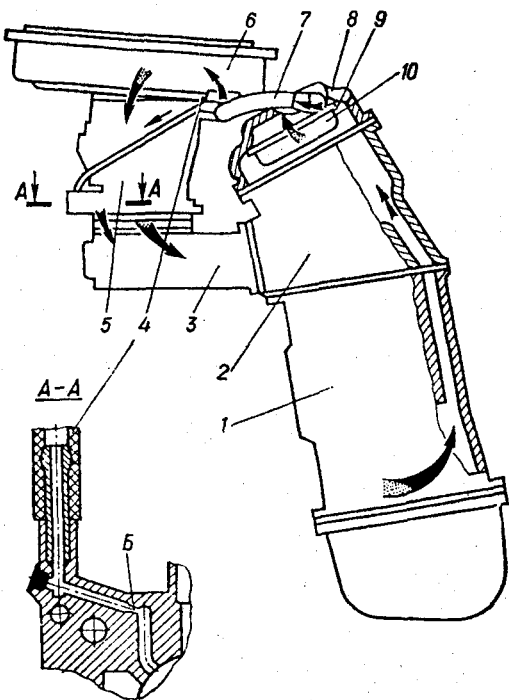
Схема системы вентиляции картерных газов: 1 – блок цилиндров; 2 – головка цилиндров; 3 – впускной коллектор; 4 – трубка отсоса картерных газов в карбюратор; 5 – карбюратор; 6 – воздушный фильтр; 7 – шланг вентиляции картера; 8 – прокладка; 9 – крышка головки цилиндров; 10 – маслоотражатель; Б – калиброванное отверстие диаметром 1,5 мм
